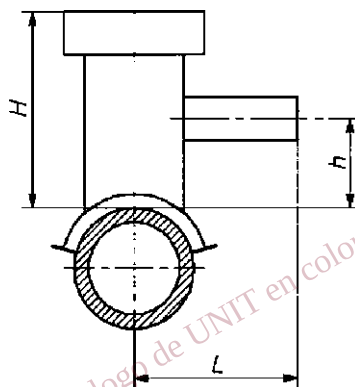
Dimensiones de los accesorios con extremo macho
